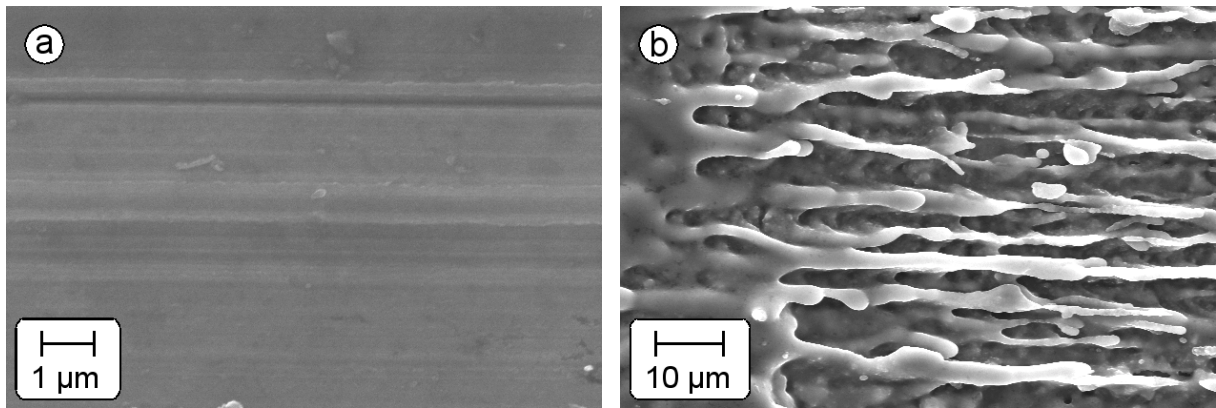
REM Aufnahmen der im Modellversuch an der Aluminiumlegierung 7075 erzeugten Werkstückoberfläche (maximal ausgehärtetes Gefüge [T 6], Schnitttiefe 200 µm): (a) $v_c = 1000$ m/min; (b) $v_c = 8000$ m/min
